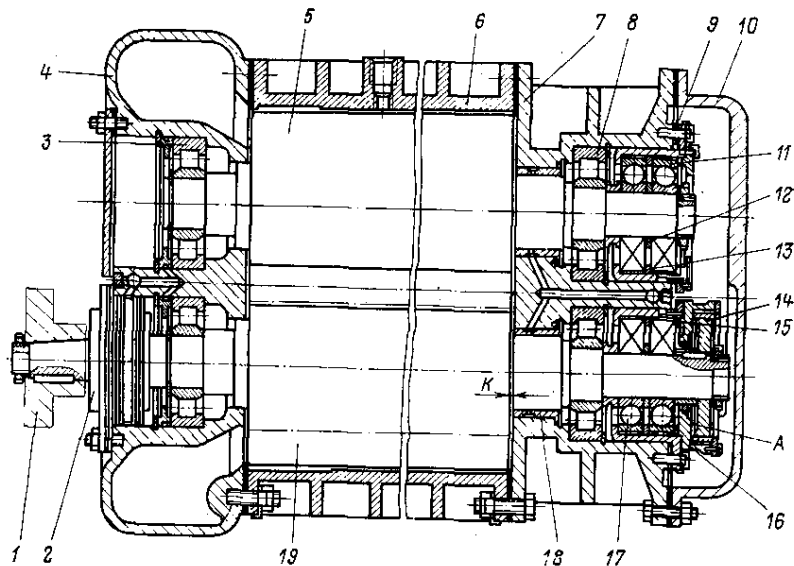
Винтовой компрессор 7ВКГ-30/7 (7ВКГ-50/7):
